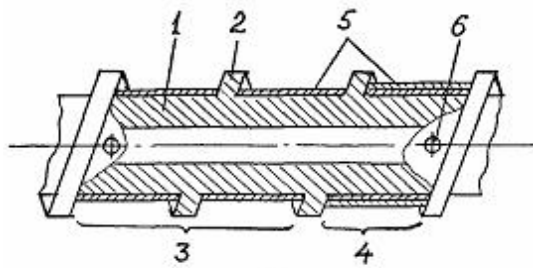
Фіг. 1 - загальний вигляд черв'яка, змішувальний елемент поза гвинтовою навивкою; Фіг. 2 - змішувальний елемент в межах гвинтової навивки; Фіг. 3 - розгортка 45 гвинтової навивки черв'яка на Фіг. 1 (стрілками показано рух розплаву).
